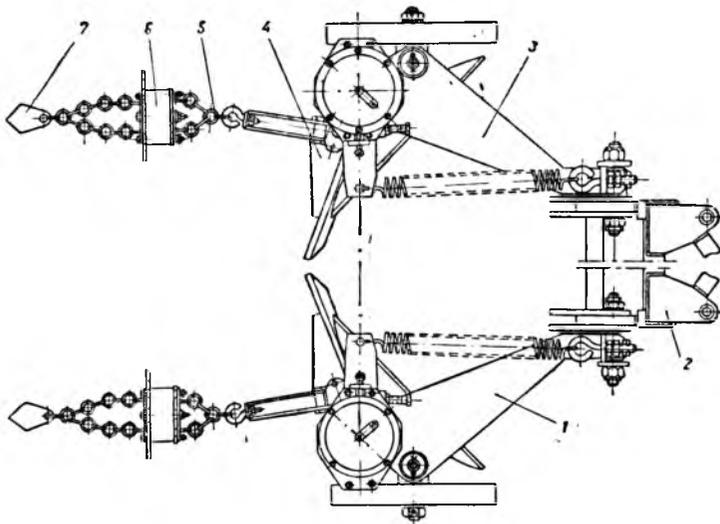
Схема покровосдирателя-сеялки ПСТ-2А: 1 — секция левая; 2 — рама навески трактора; 3 — секция правая; 4 — перо; 5 — тяга боронки; 6 — боронка; 7 — шлейф.
